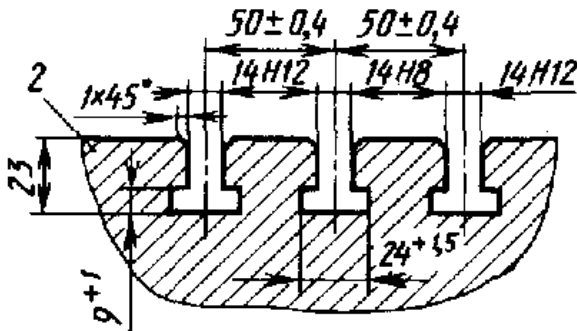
Посадочні розміри робочого столу вертикально - свердлувального верстату моделі 2Н118
